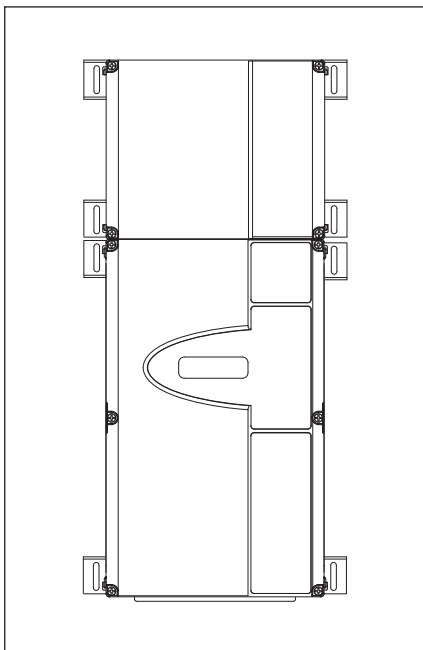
Корпус блока управления и дополнительный корпус с горизонтально закрепленными монтажными опорами
